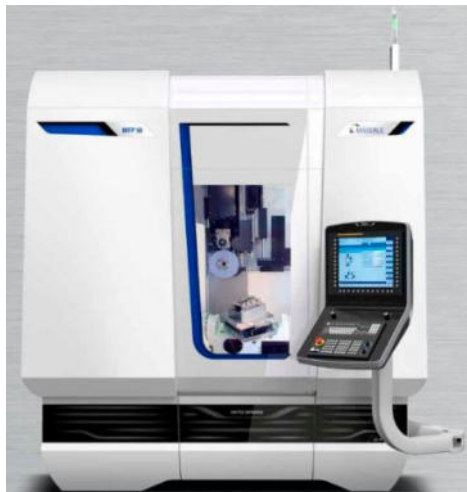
Внешний вид пятиосевого профилешлифовального станка MFP-050.65.65 фирмы «Mägerle»
